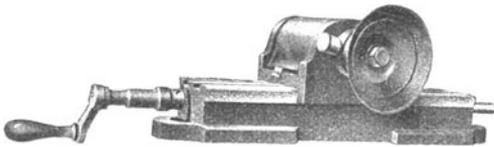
Abrichtapparat für Sandsteine mit Glockenmesser.
